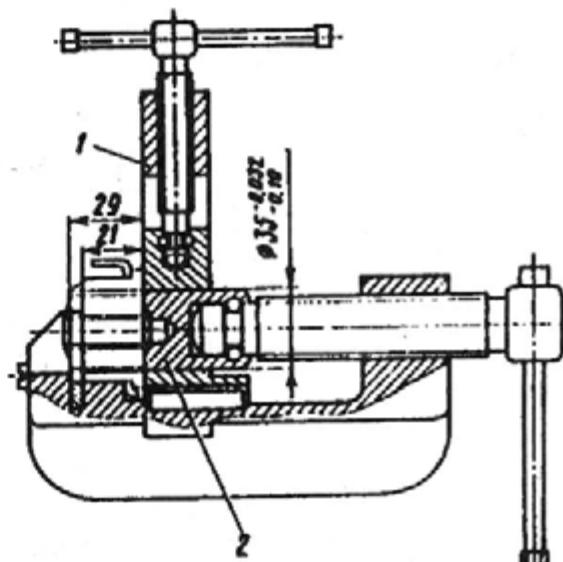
Приспособление 9680-3272 для запрессовки сайлент-блока в верхний рычаг:
